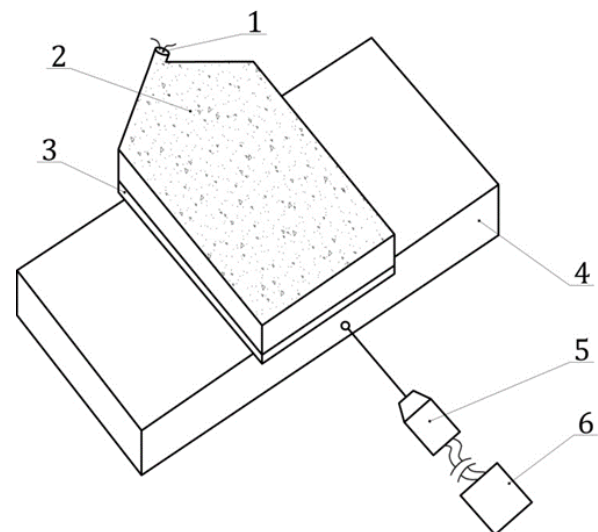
Схема сварки взрывом с одновременным воздействием ультразвука переходника: 1 – электродетонатор; 2 – заряд ВВ; 3 – метаемая медная пластина; 4 – неподвижная алюминиевая пластина; 5 – пьезокерамический преобразователь; 6 – ультразвуковой генератор
